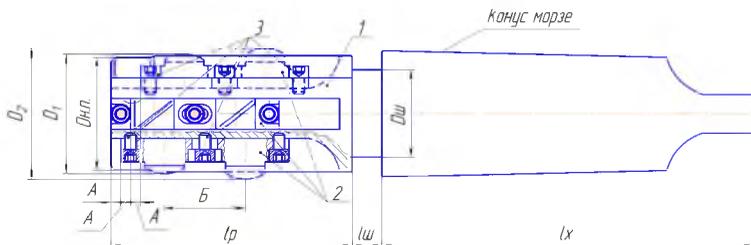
Общий вид резцовой сборной развёртки со сдвоенными безвершинными зубьями с разными диаметрами
